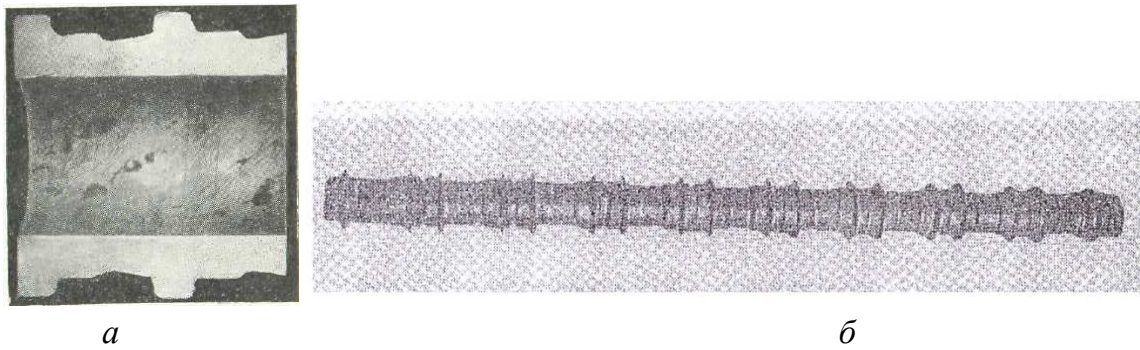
Вид заготовок с РПП: а- микрошлиф ; б- вид заготовки с РПП для велосипедной втулки
